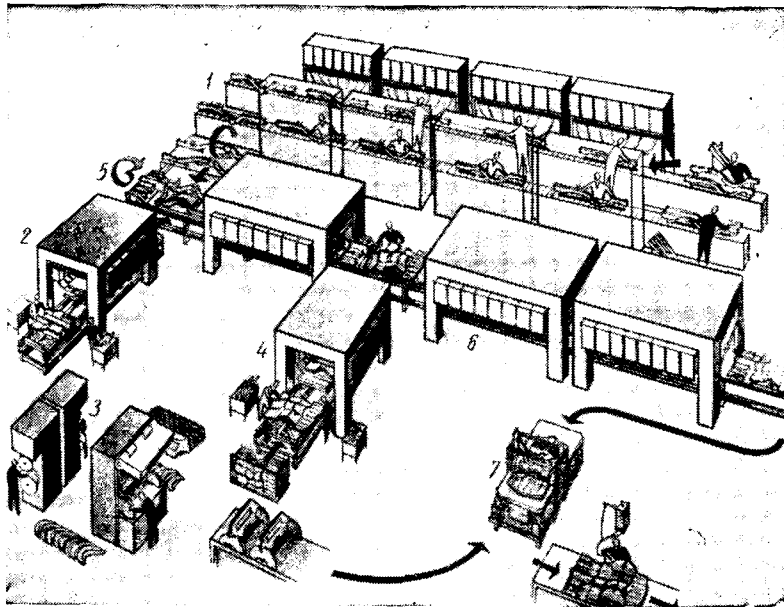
Участок сварки заднего пола автомобильного кузова и схема движения деталей и узлов:
